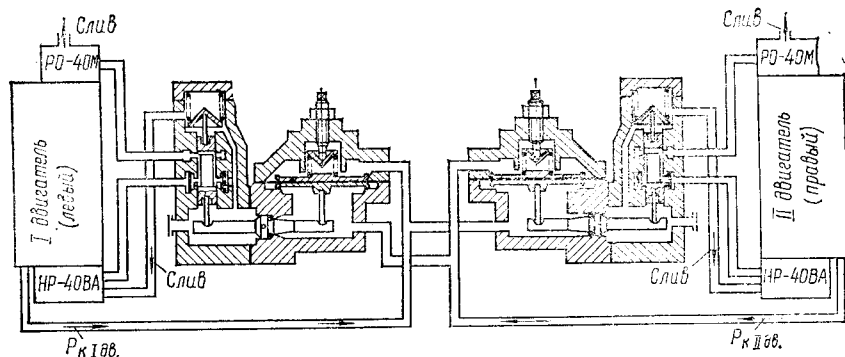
Схема установки агрегатов СО-40 на спаренных двигателях вертолета:
